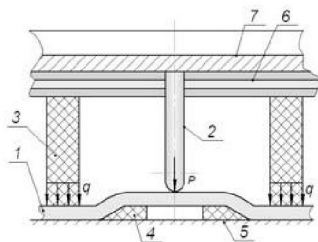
Схема фрагменту прес пари для бігування картонної заготовки: 1 — картонна заготовка; 2 — бігувальна лінійка; 3 — еластичний прижим; 4 — бігувальна матриця; 5 — контрматриця; 6 — вирубний штамп; 7 — сталеві пластини
